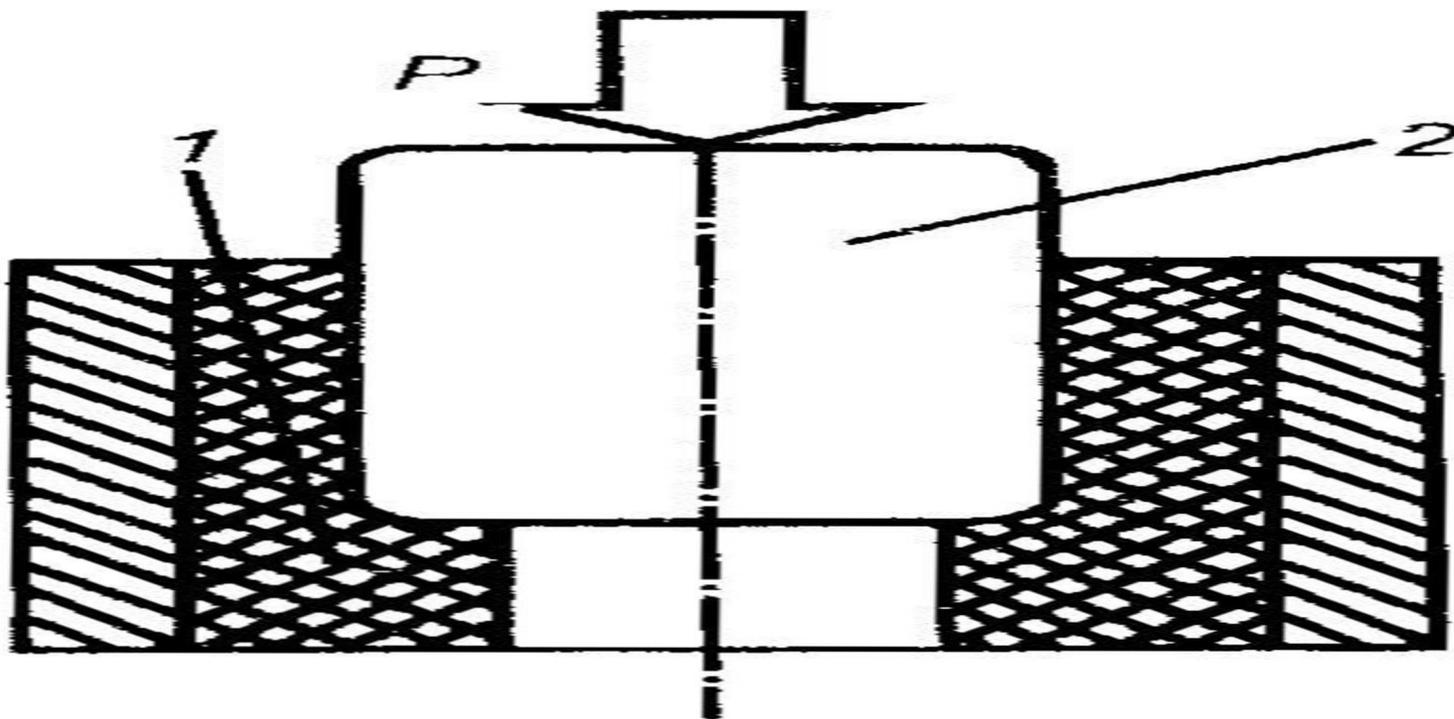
Схема восстановления детали калиброванием: 1 — полимерное покрытие; 2 — калибр
